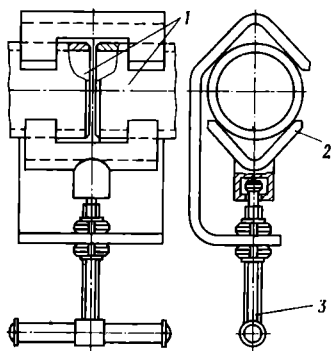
Сборка стыка труб с помощью центровочного приспособления:
